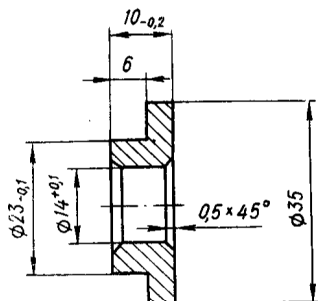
Оправка для запрессовки сальников в картер рулевого механизма
